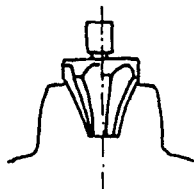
Frézovanie zubovej medzery kotúčovou modulovou frézou
